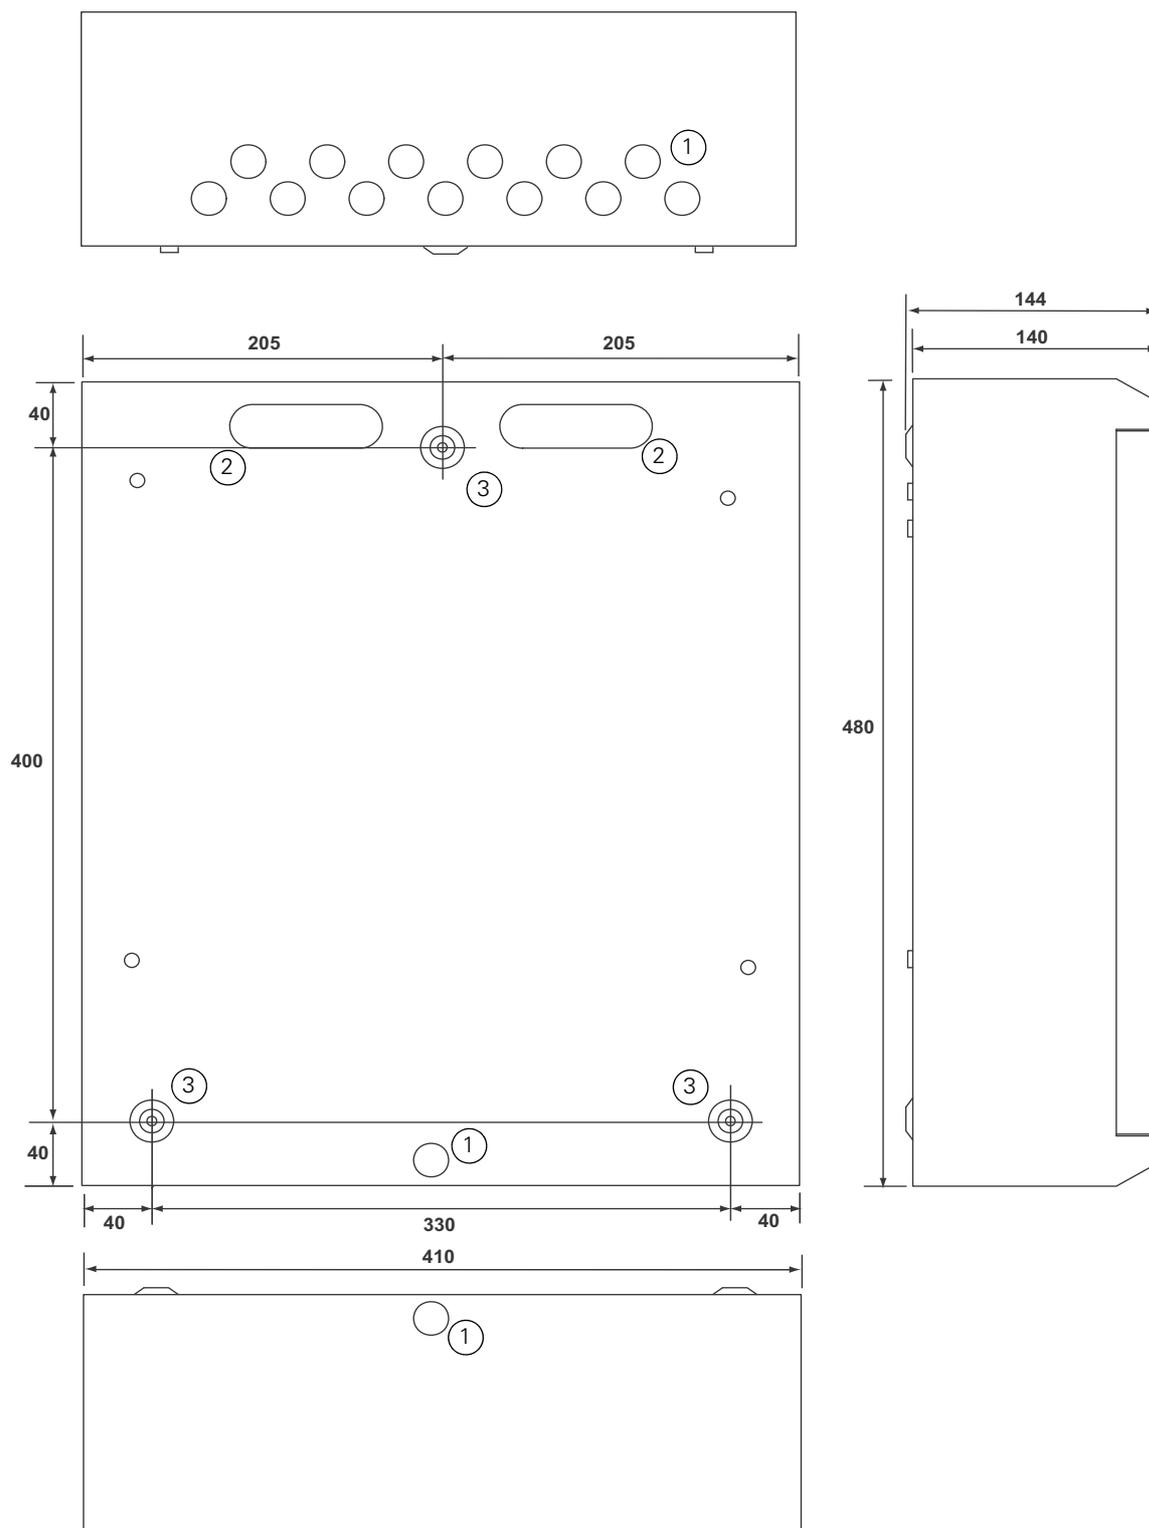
Dimensioni generali e di fissaggio – 240-2, ripetitori 240RA
